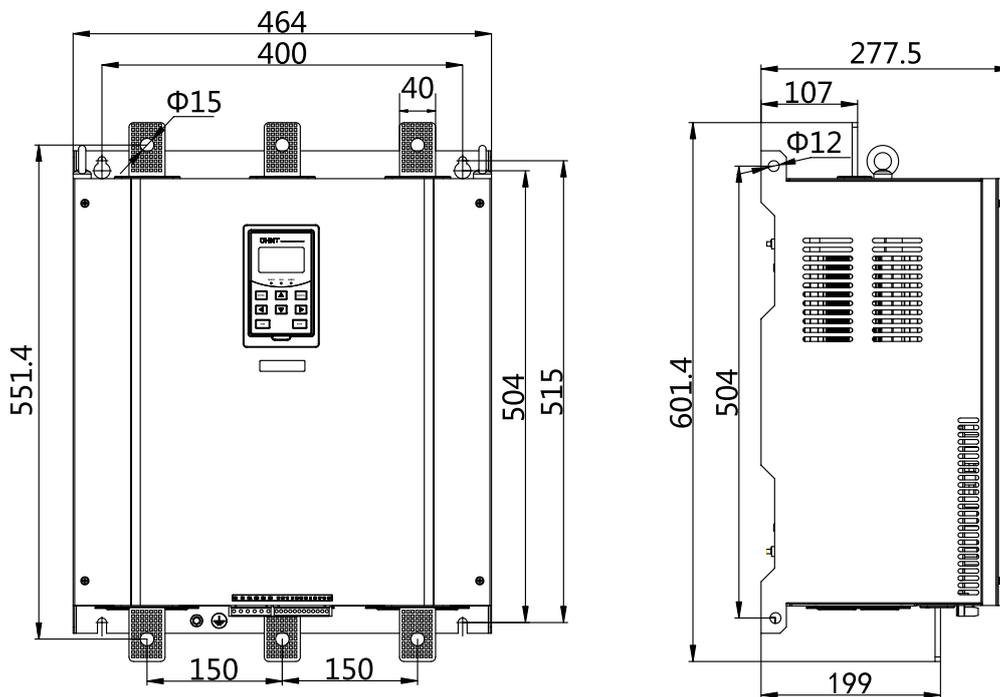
Общий компоновочный и установочный габаритный чертеж для устройств моделей NJR5-440/ZX3–NJR5-710/ZX3 и NJR5-440/ZX6–NJR5-710/ZX6
